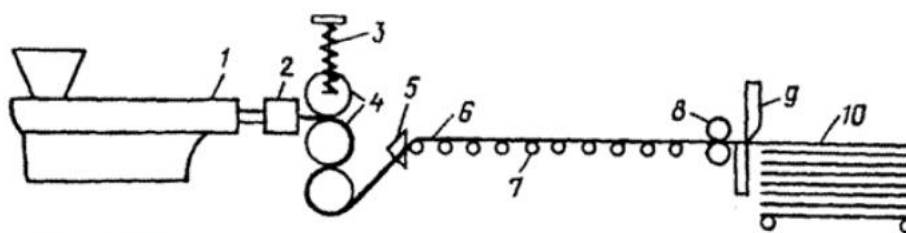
Технологическая схема агрегата для получения листов: 1 – экструдер; 2 – листовальная головка; 3 – механизм для регулирования зазора между валками; 4 – гладильно-калибровочные валки каландра; 5 – ножи для обрезки кромок; 6 – лист; 7 – рольганг; 8 – тянущее устройство; 9 – гильотинный нож; 10 – штабель листов
